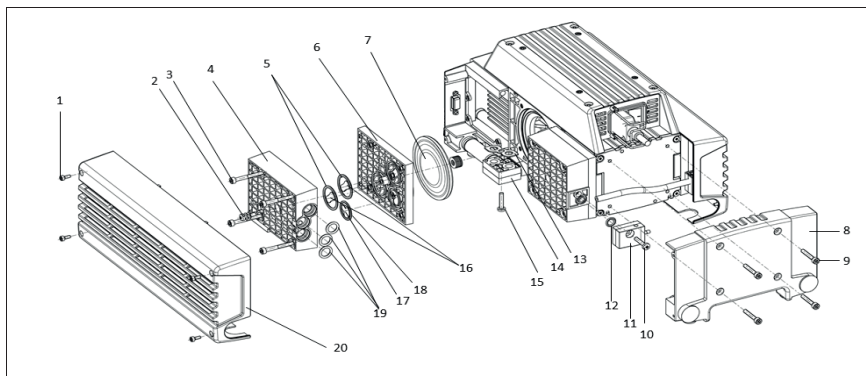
Explosionszeichnung PJ25481-950.50.18
